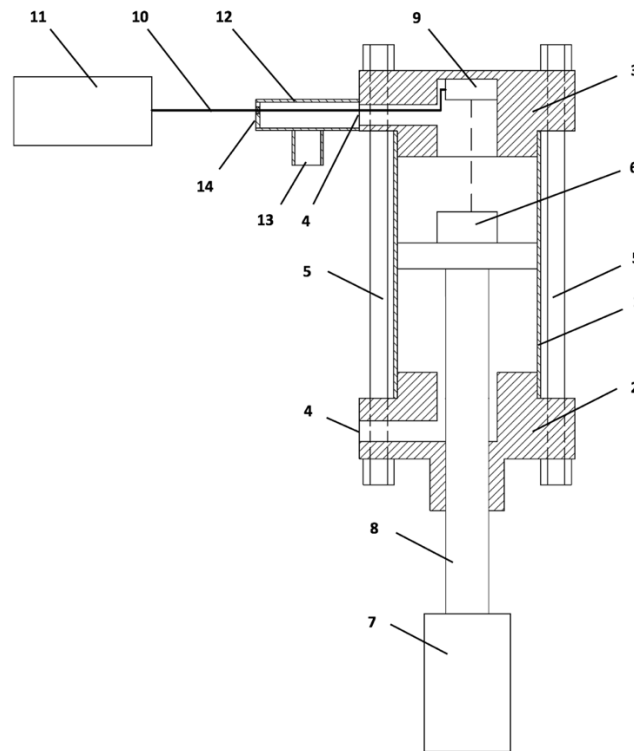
Схема установки оптического дальномера в мертвый объем пневмоцилиндра: 1 – корпус; 2 – передняя крышка; 3 – задняя крышка; 4 – отверстия; 5 – крепеж; 6 – поршень; 7 – наконечник; 8 – шток; 9 – оптический дальномер; 10 – кабель; 11 – контроллер; 12 – тройник; 13 – вывод для подключения пневмолинии; 14 – герметичный ввод
